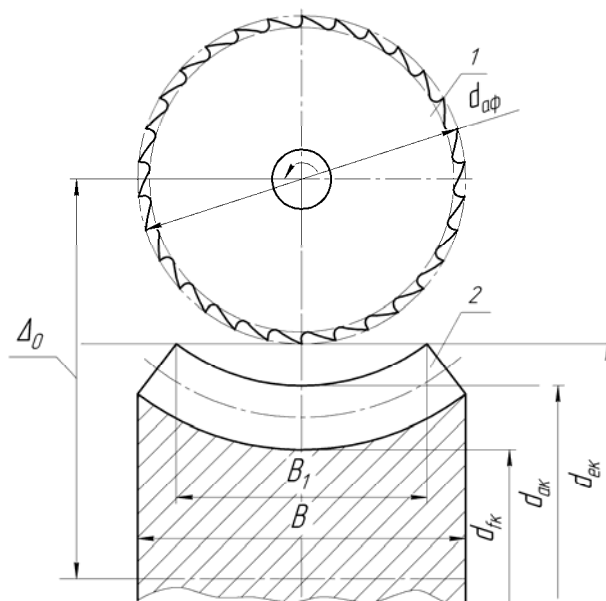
Початкове положення дискової фрези (1) ($z=30$; $m=1,6$; $b=2$) стосовно оброблюваного глобоїдного черв'ячного колеса (2)
